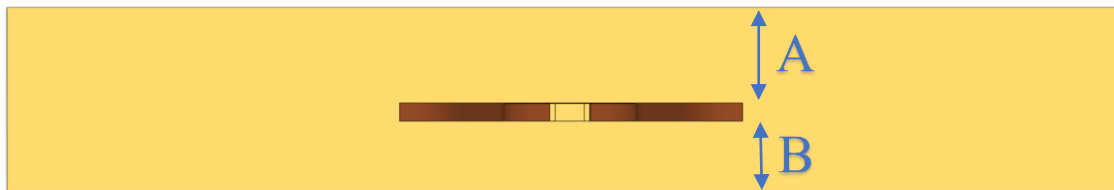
bloque del dispositivo a fabricar mediante la técnica *diffusion bonding*. Vista alzado.
